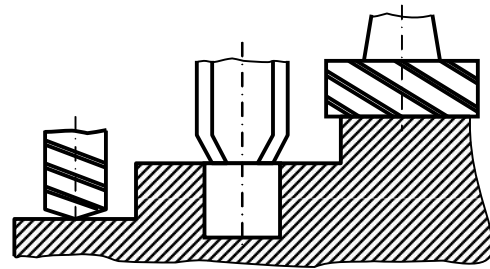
Схема настроювання вильоту інструментів, що обробляють різні поверхні одної заготовки
